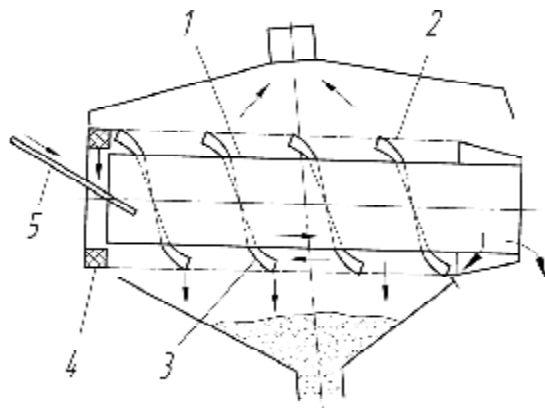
Галтовочный барабан непрерывного действия для очистки отливок
